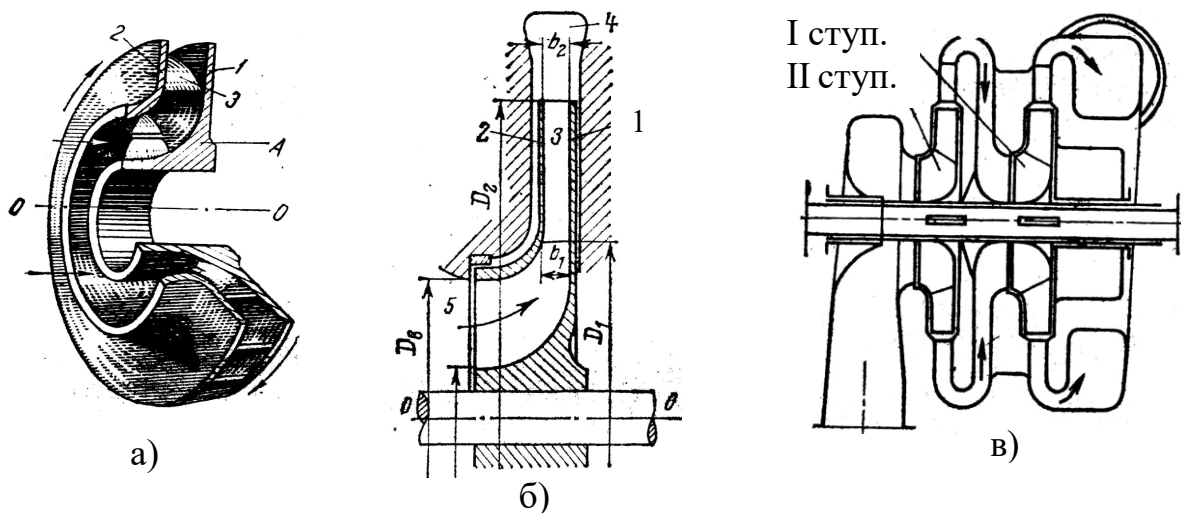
Схеми відцентрового компресора: а – робоче колесо машини; б – переріз колеса; в – двоступінчастий відцентровий компресор
